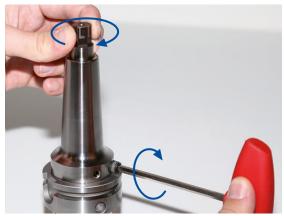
Ruotare la vite di serraggio e l'utensile di prova
